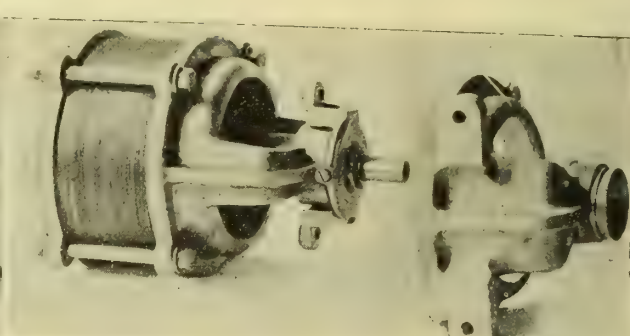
Moteur de T. S. F. à flasques d'aluminium.
